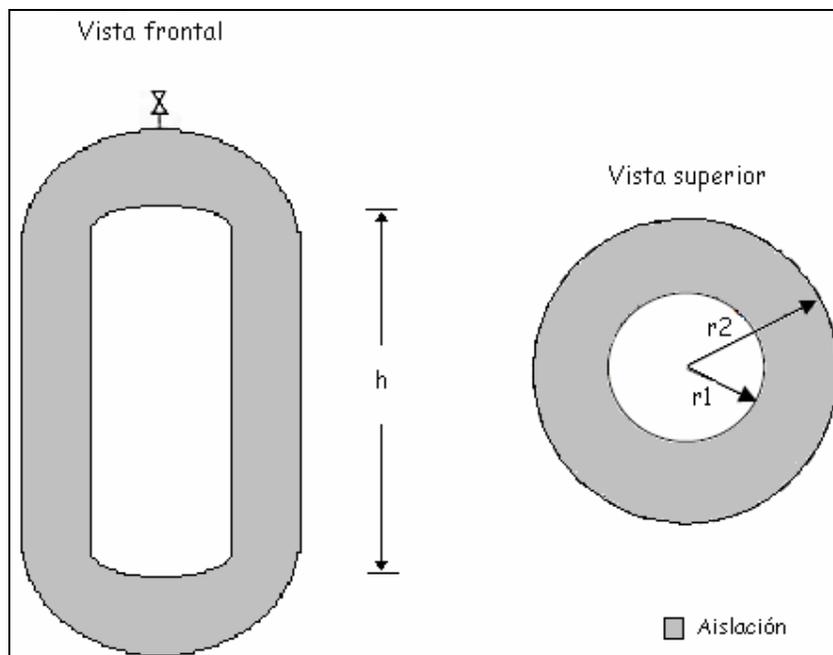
Dimensiones del estanque de almacenamiento LIN.
